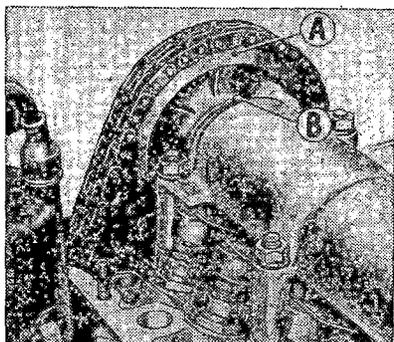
Установка поршня четвертого цилиндра в положение ВМТ в конце такта сжатия по меткам на звездочке и корпусе распределительного вала
